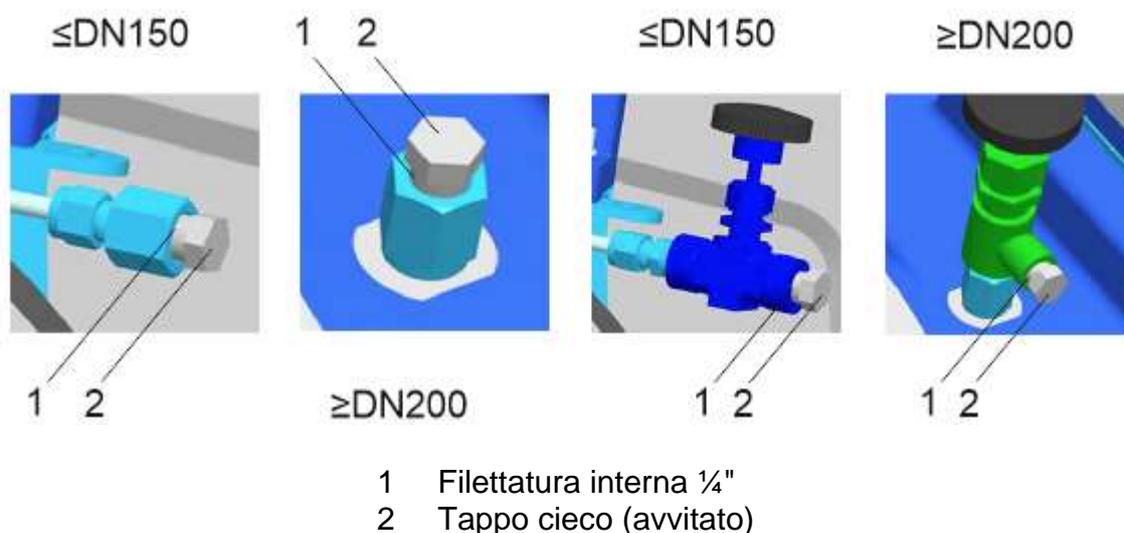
Possibilità di connessione del collegamento in pressione con filettatura interna
